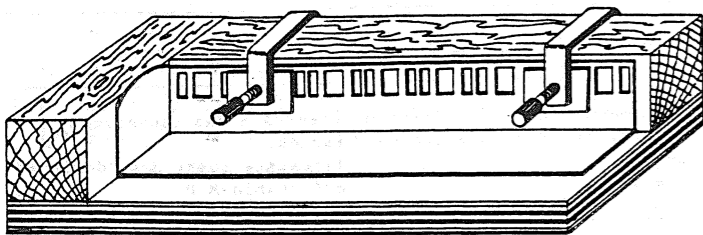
Maintien en position de soudure d'éléments de caisse de voiture. Serre-joints omis sur plancher et dossier pour plus de clarté.
